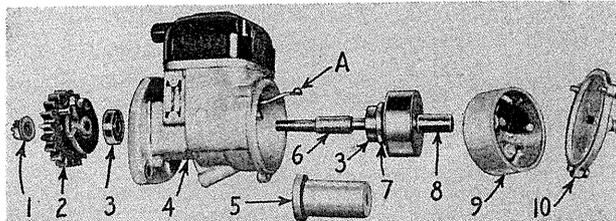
MAGNETO "AH", ROTOR DEMONTÉ. 1 - ECRU DE
